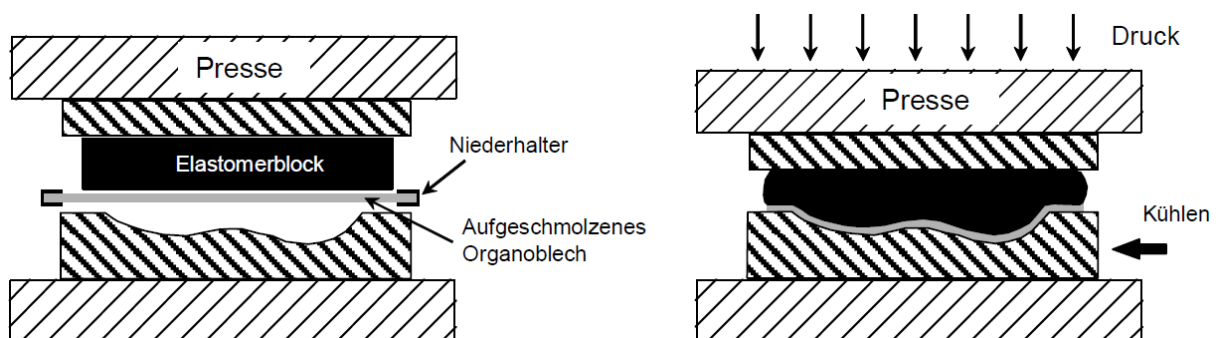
Thermoformen mit Elastomerblock [40]
